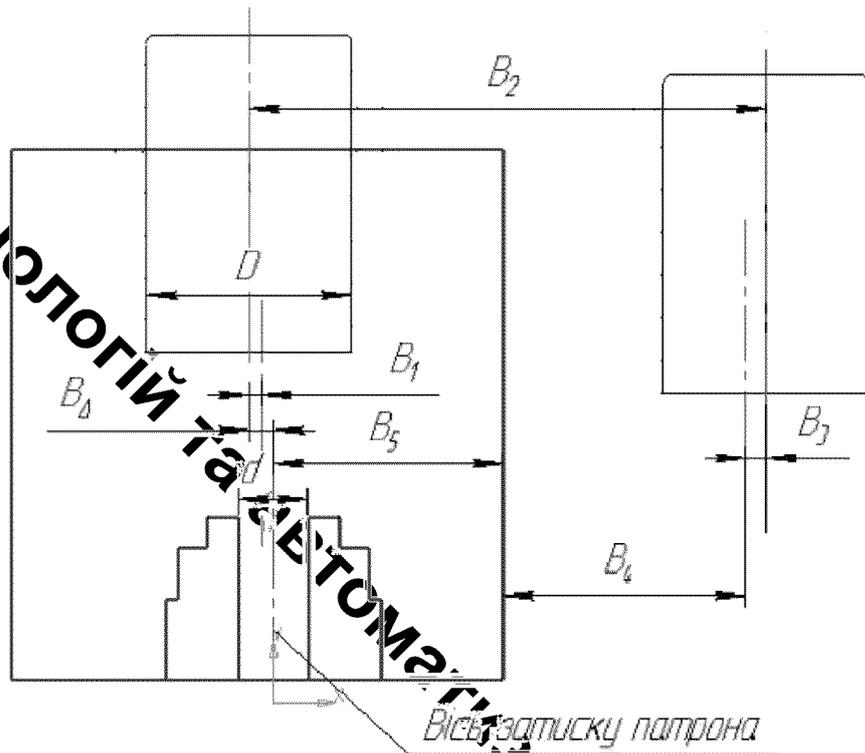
Розрахунок похибки розміщення заготовки деталі «Вал-шестерня Д02210.5»
